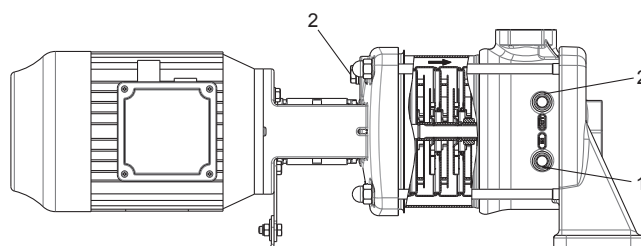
Anschlüsse zum Entleeren der Pumpe
